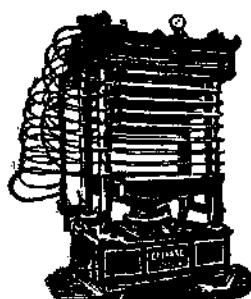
Гидравлический kleильный пресс с горячими плитами.
